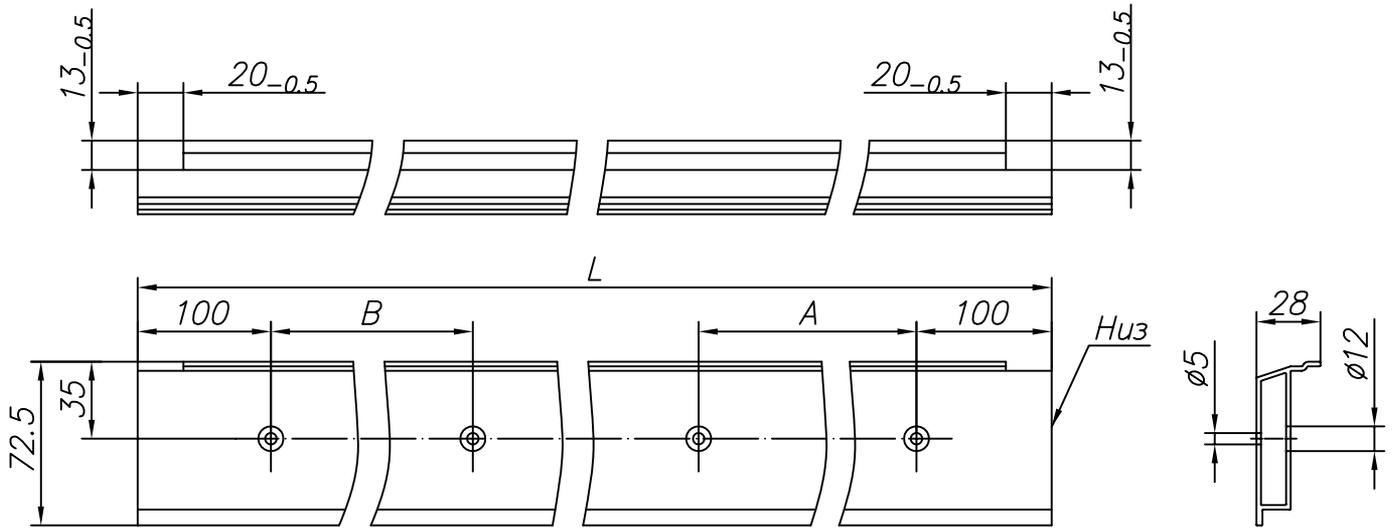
Изготовление притвора без паза для ответной пластины замка из профиля FLGU.400.0505 (открытие внутрь)
